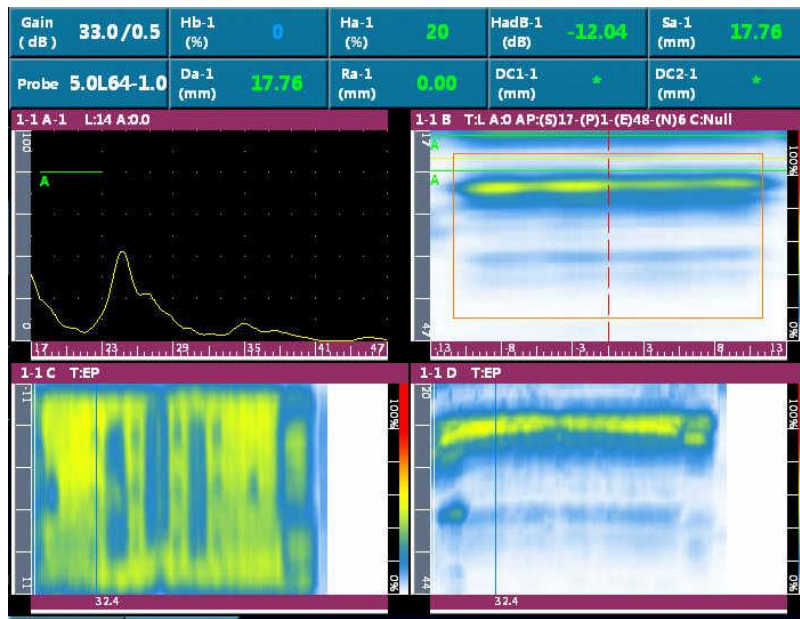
Medição Def. B HOLPF-32-6-M
